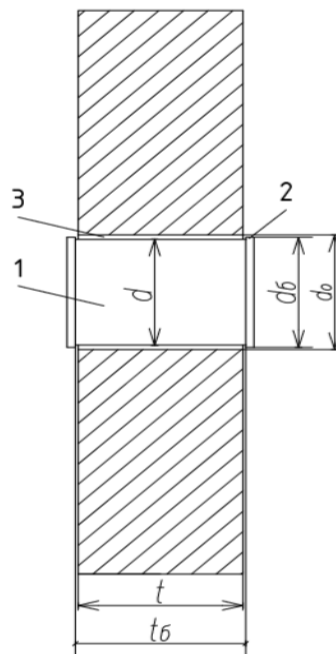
Інструмент із циліндричними буртами для зміцнення отворів: 1 – робочий інструмент із сплаву із пам'яттю форми; 2 – бурти інструменту; 3 – отвір пластини [126]
